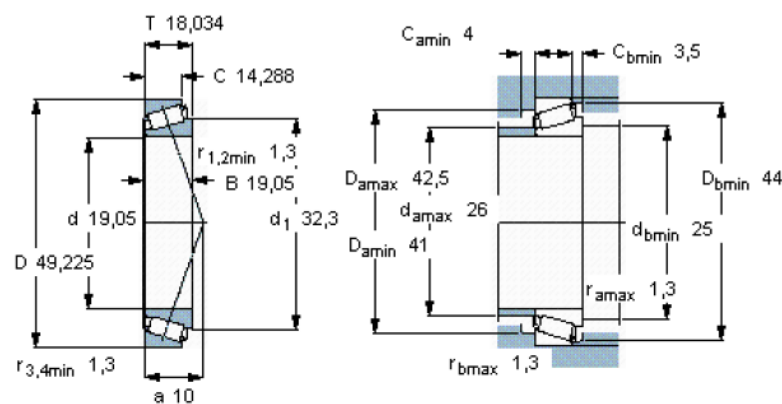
Dimensiones del cojinete 09067/09195/Q [14].
